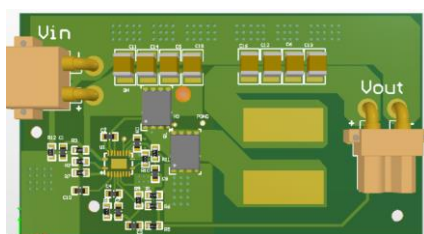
2023 赛季 48V 转 24V 稳压模块 PCB
